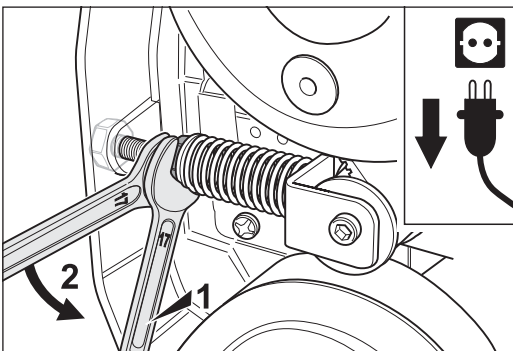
Mit einem Gabelschlüssel die Spannmutter festhalten (1) und gleichzeitig mit einem zweiten Gabelschlüssel die Kontermutter gegen die Spannmutter schrauben (2), so dass beide Muttern fest gekontert sind.
